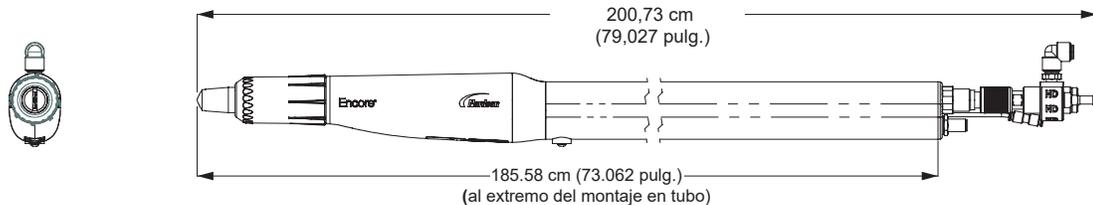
Dimensiones y pesos de las pistolas de montaje
